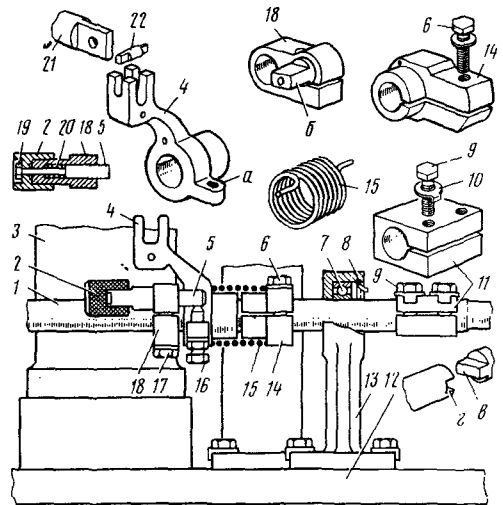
Соединение реек топливных насосов: 1 — вал управления топливными насосами; 2 — головка; 3 — топливный насос; 4 — ловодок; 5 — фиксатор; 6, 9, 17 — стяжные болты; 7 — шариковый подшипник; 8 — стопорное кольцо; 10 — шайба; 11 — хомут; 12 — верхний горизонтальный лист отсека распределительного вала; 13 — стойка; 14, 18 — правый и левый комутики; 15, 20 — пружины; 16 — регулировочный болт; 19 — гайка; 21 — зубчатая рейка; 22 — палец; *б, в* — выступы; *г* — паз
